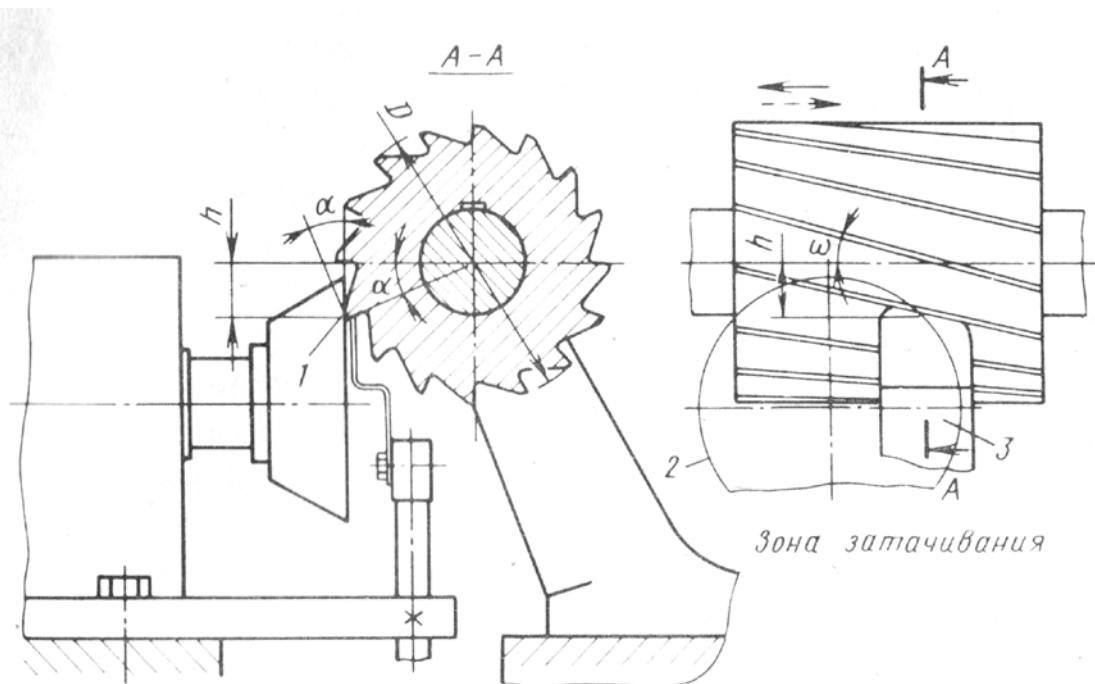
Схема установки фрезы при образовании главных задних поверхностей:
